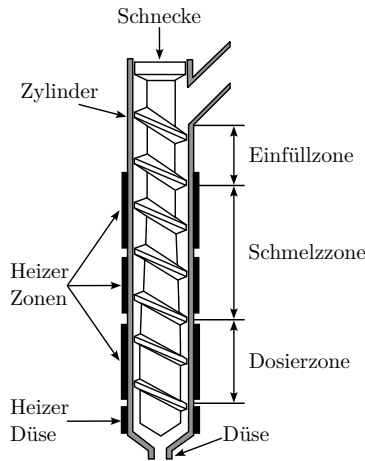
Prinzipskizze eines Einschneckenextruders für den FGF-Prozess [28, 38]
